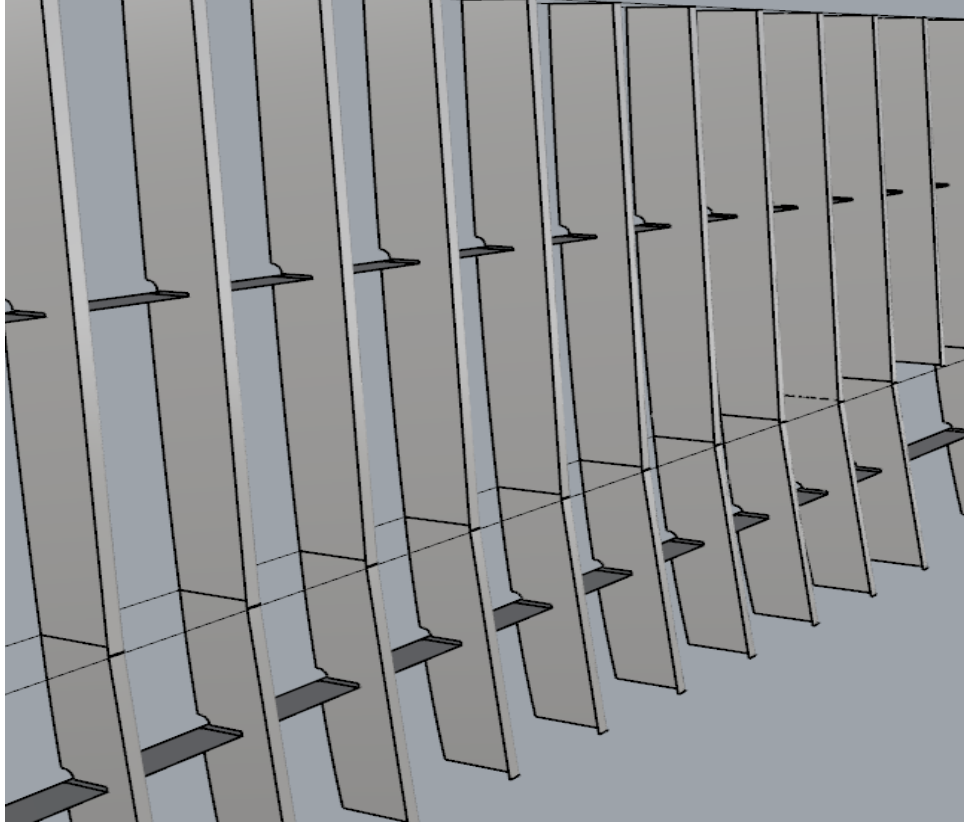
Postalar, posta laması ve boyuna elemanın detaylı görünümü
